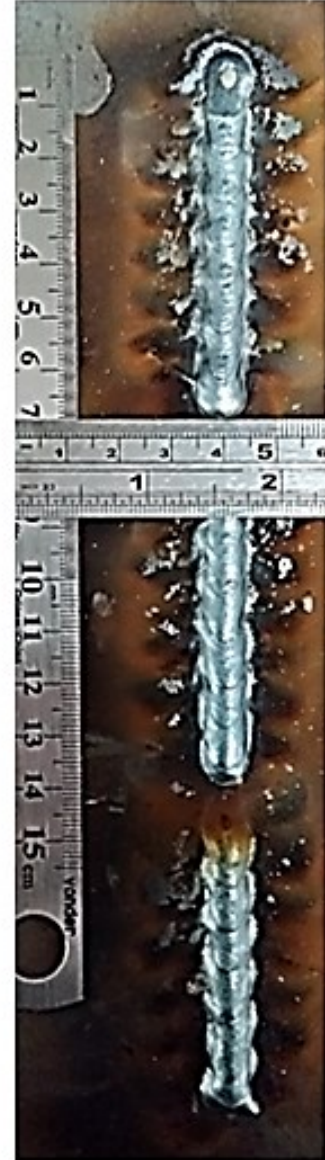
Soldagens GMAW pulsada. Com oscilação do arco Bx=10 mT
